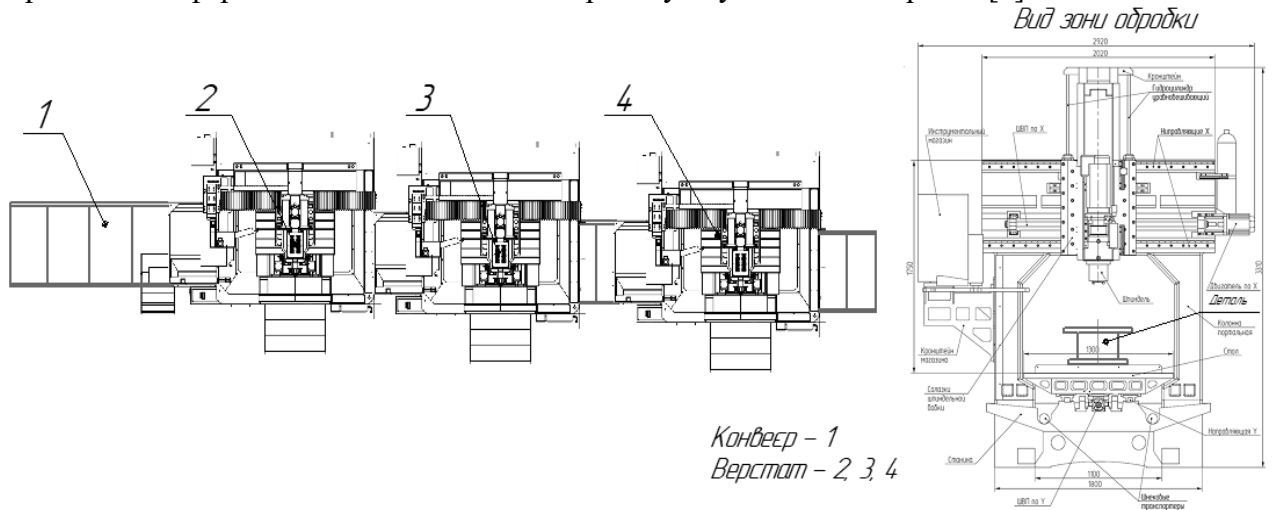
Компонувальна схема обробки деталі «корпус»
